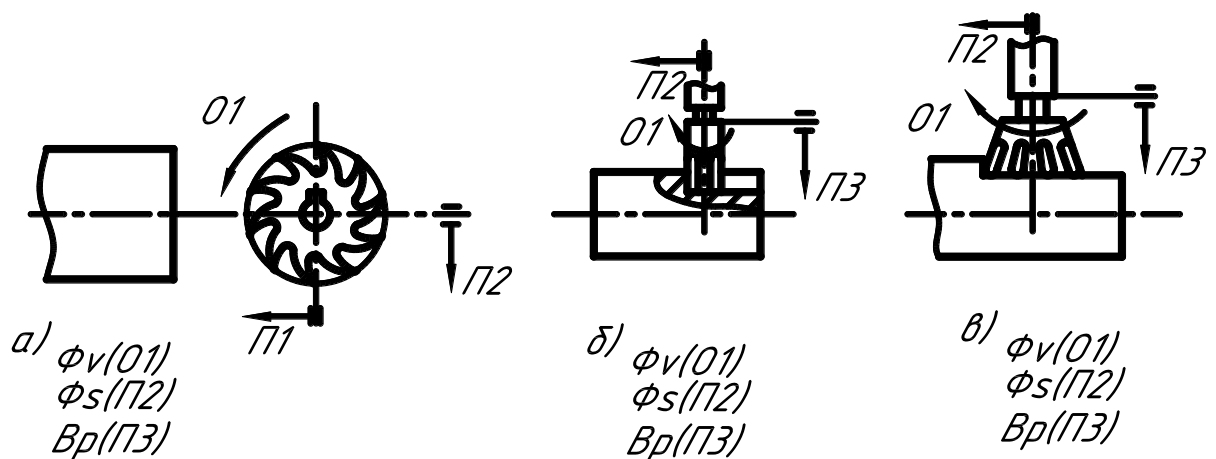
Схеми формоутворення поверхонь деталей фрезеруванням на токарному верстаті.
